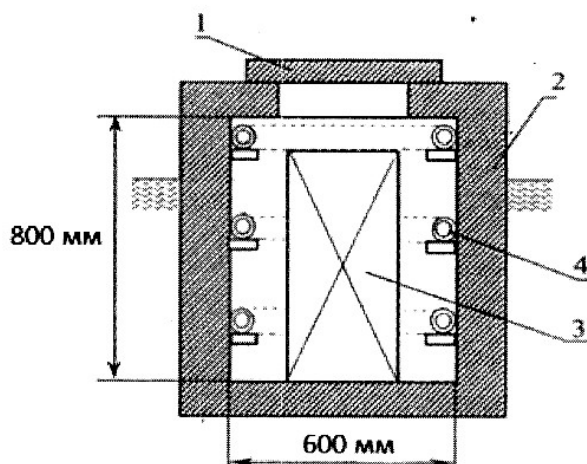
Шахтная печь: 1-крышк; 2- футеровка; 3- нагреваемое изделие; 4 – нагреватель.
